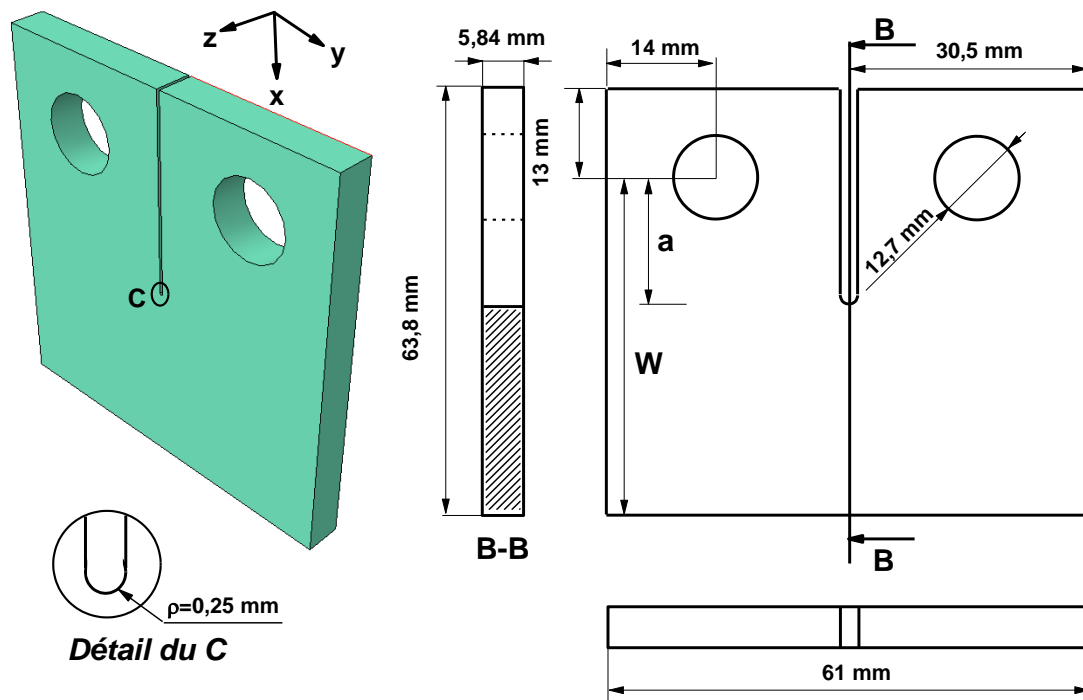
Géométrie et dimensions de l'éprouvette étudiée
